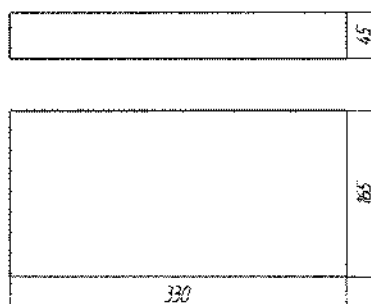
Эскиз заготовки (плита Д16 Б 50)
